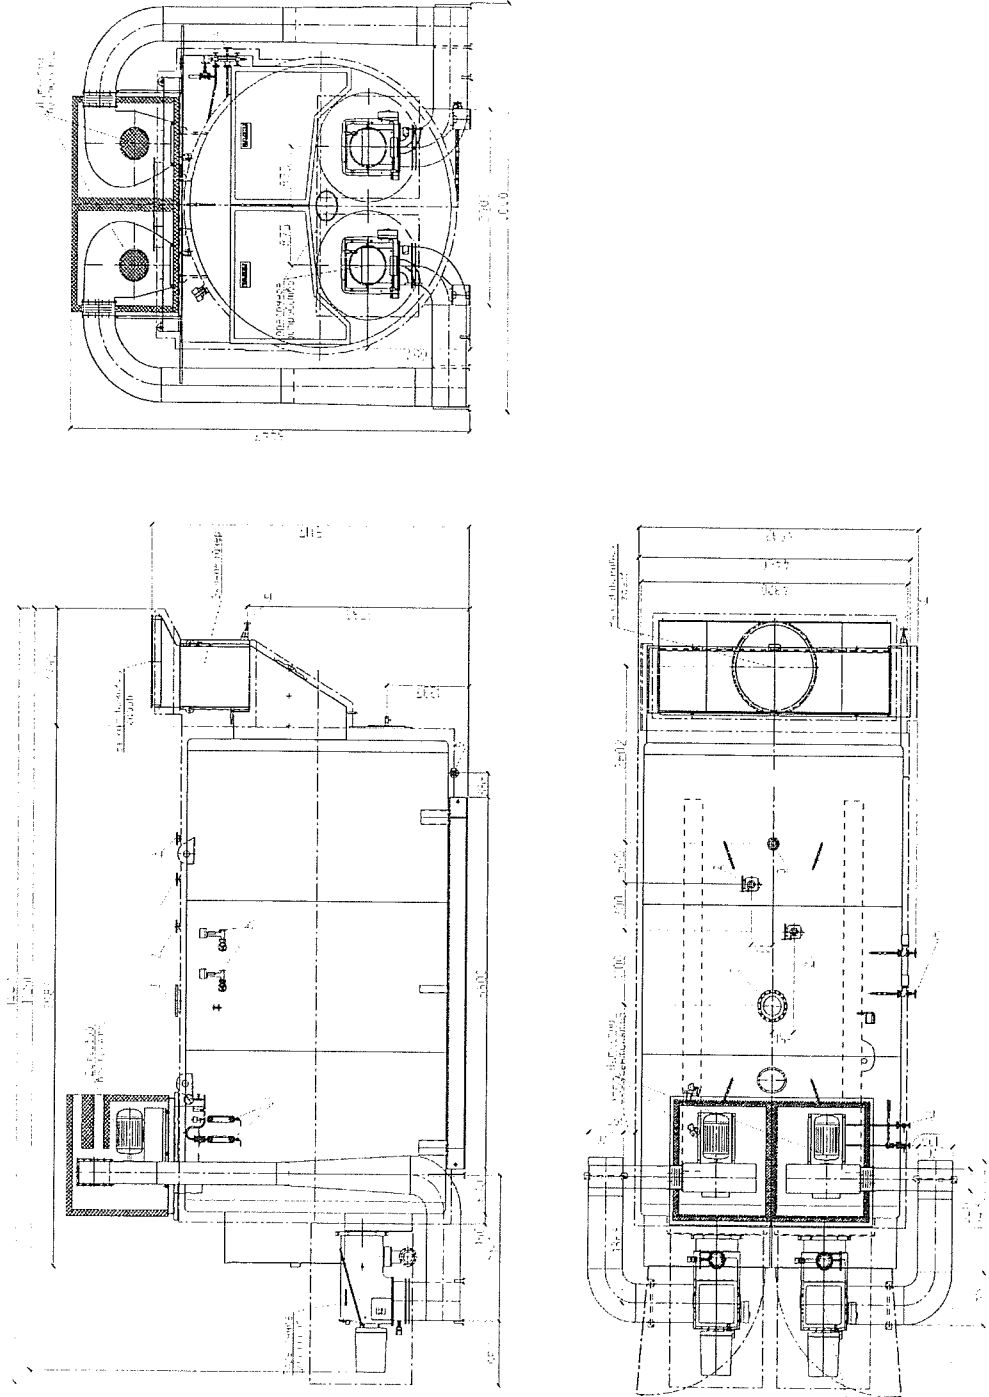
Габаритные размеры котла парового по типу LOOS UNIVERSAL, тип ZFR
